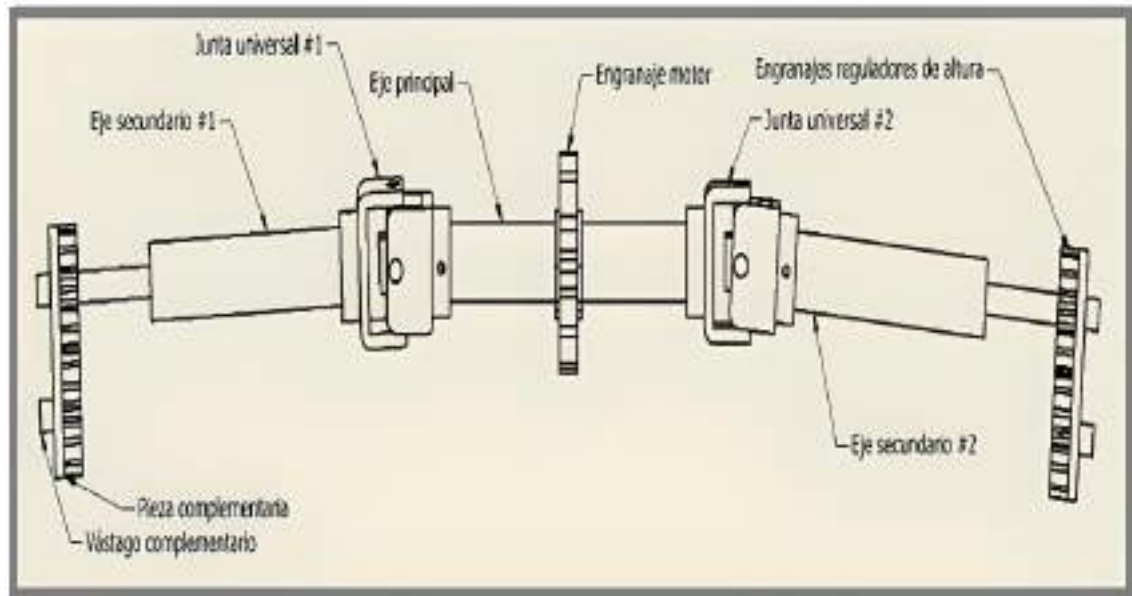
Mecanismo vinculando del motor impulsor a engranajes regulador de altura. Fuente: elaboración propia.
